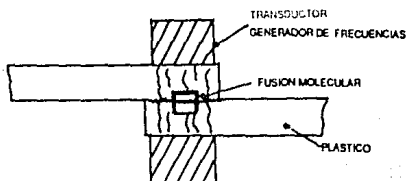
Soldadura ultrasónica. (Ref. 8).
